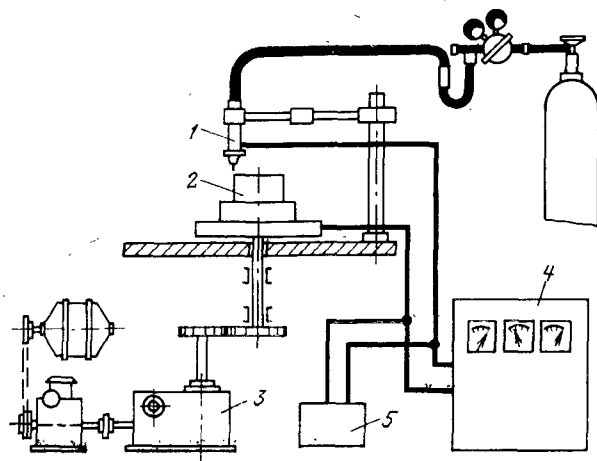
Схема установки для аргодуговой сварки с местным обдувом.
